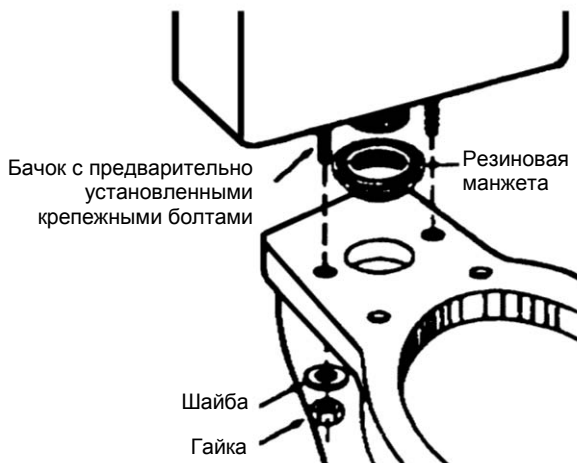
Монтаж бачка с предварительно установленными болтами (American Standard)
